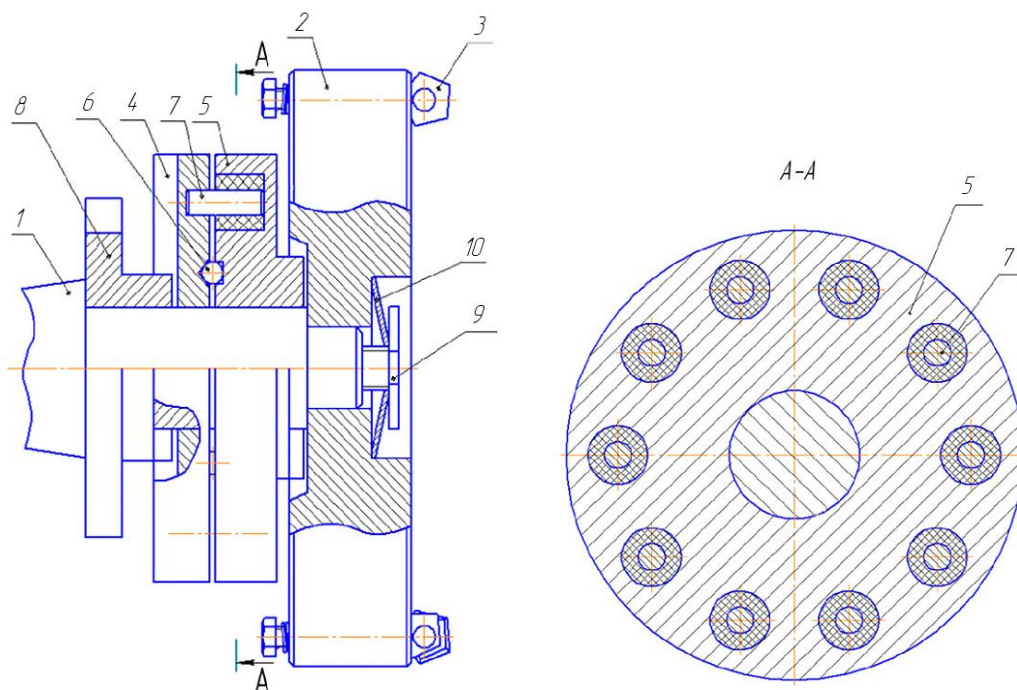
сборная торцевая фреза с демпфирующими элементами: 1- оправка; 2- фреза торцевая; 3-режущие ножи; 4- верхнее кольцо узла демпфирования; 5- нижнее кольцо узла демпфирования; 6-стальные шарики; 7-
